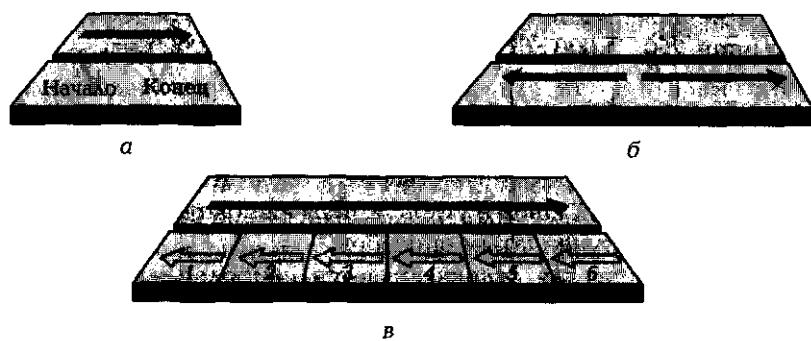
Способы выполнения сварных швов по длине:
